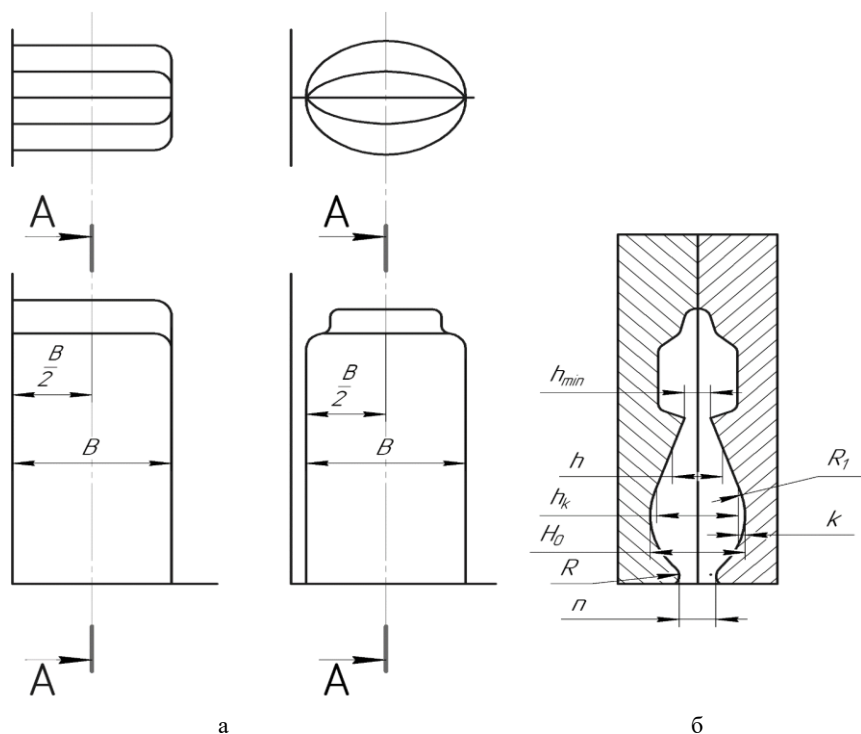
Подкатные ручки: а – открытый; б – закрытый
